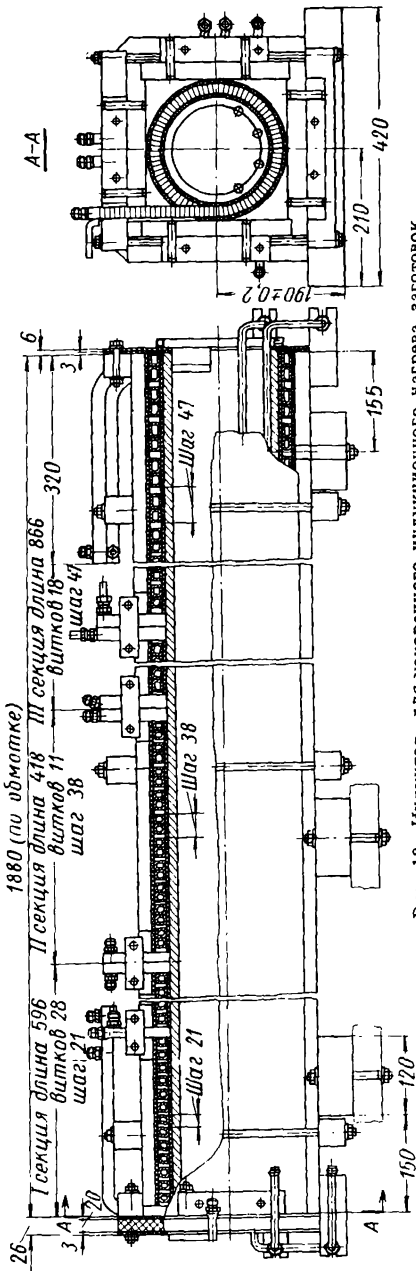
Индуктор для ускоренного индукционного нагрева заготовок
